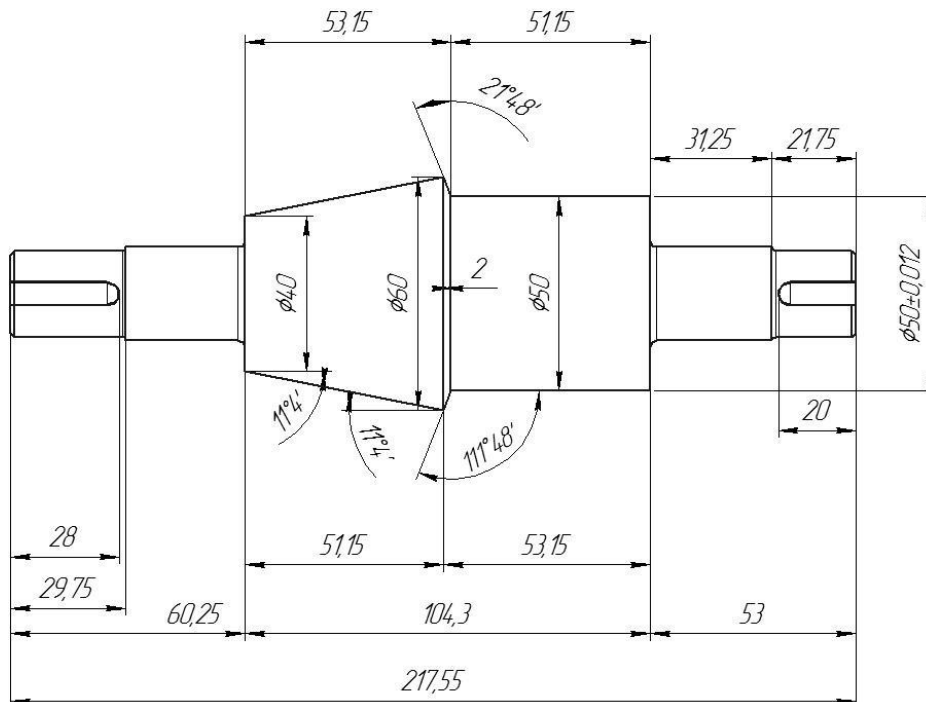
Рабочий валок с обратной конусностью стана ДУО50
